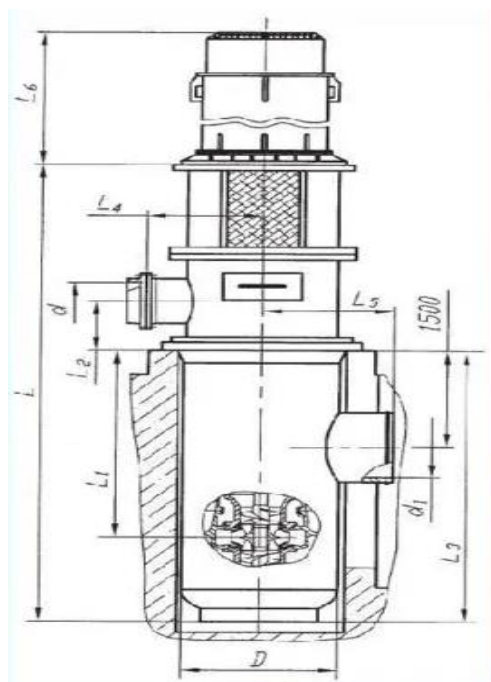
Конструктивно-принципова схема насоса НМП 2500-74
